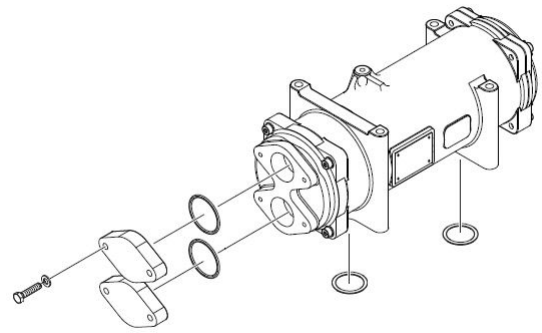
Aufbau Getriebeölkühler (Beispiel)
